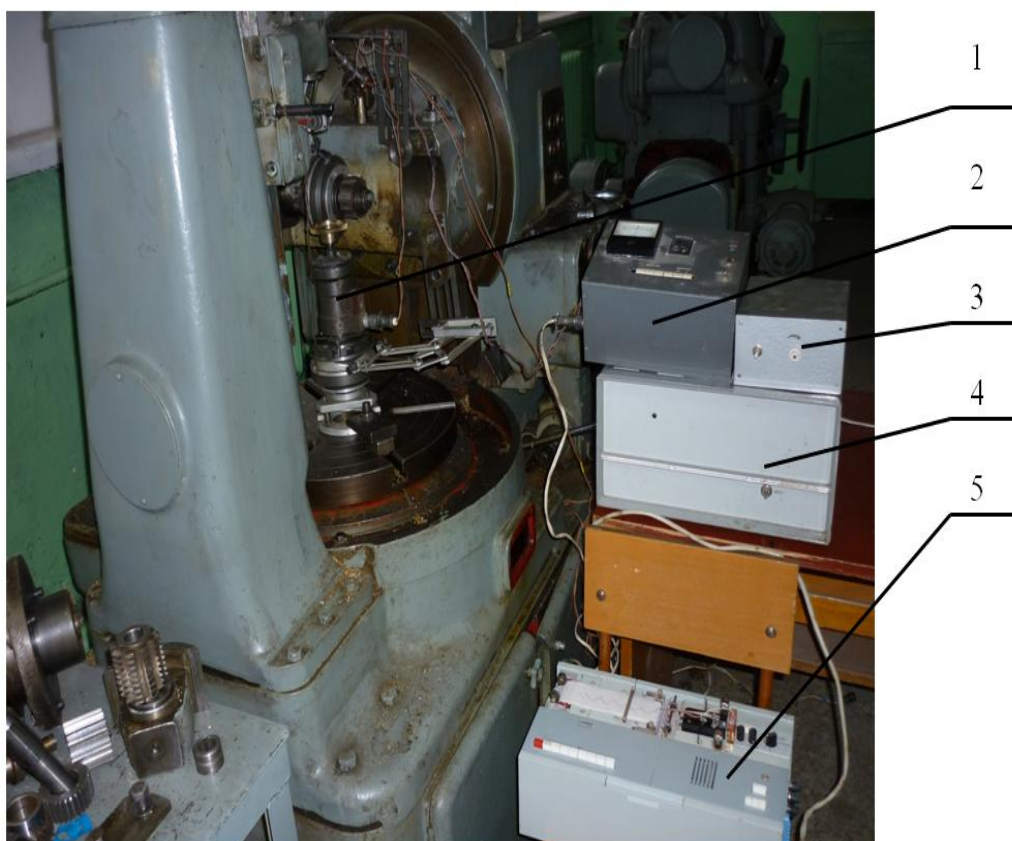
Установка для измерения кинематической погрешности зубчатого колеса в процессе его изготовления:
